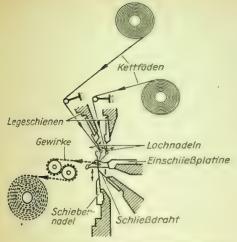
Prinzip einer Kettenwirkmaschine
